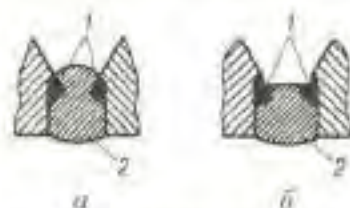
Шліфування кореня шва зобразованим колом:
